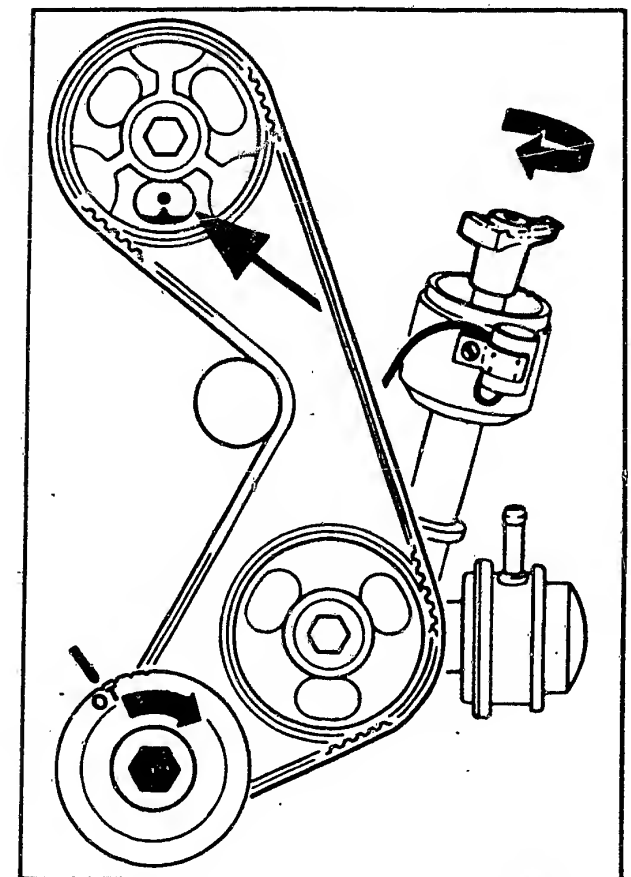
Motorsteuerung. OT-Markierungen von Nockenwellen- und Kurbelwellenzahnriemenrad. Der Verteilerrotor zeigt auf die Kerbmarke im Gehäuse.
